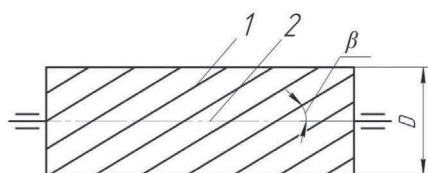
Схема к определению угла наклона планки: 1 – планка; 2 – ось катка
